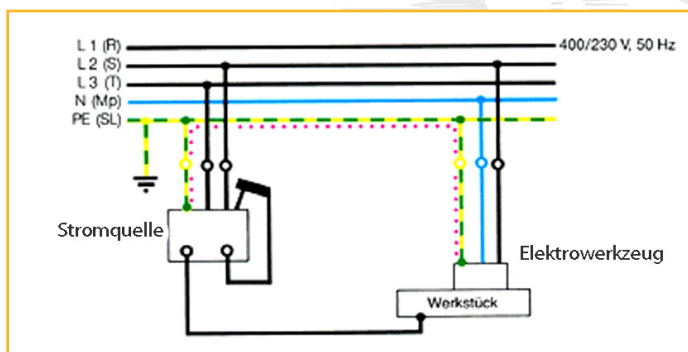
Wenn der Elektrodenhalter mit eingespannter Stabelektrode unzulässig nicht isoliert auf der Schweißstromquelle abgelegt wird, können durch den Schweißstrom die Schutzleiter von Elektrowerkzeug und Schweißstromquelle durchbrennen. Der Weg des vagabundierenden Schweißstromes ist punktiert.
